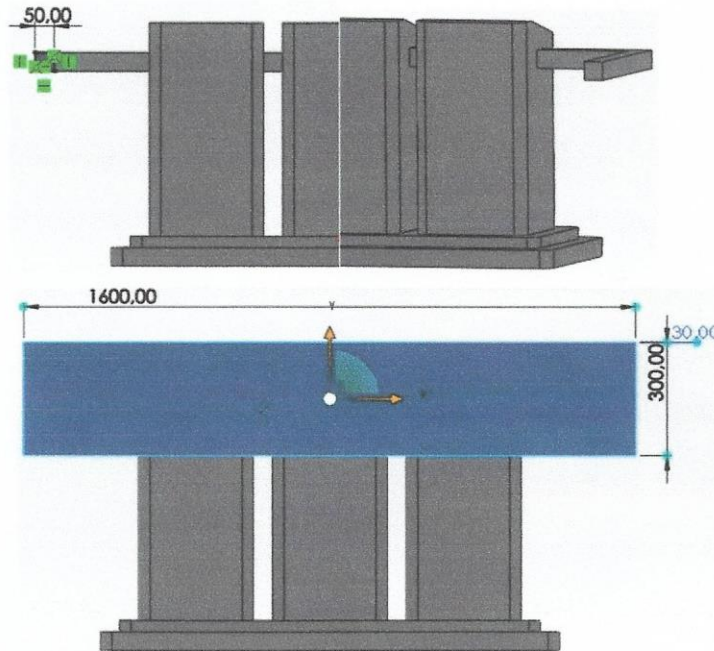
VISTA DE LA CONEXION DEL CONTENEDOR
